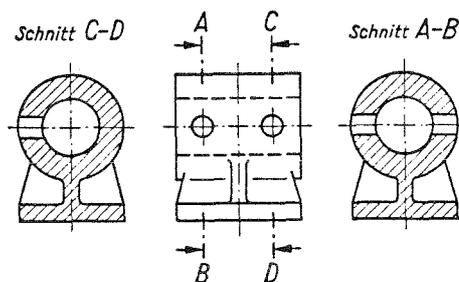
Hinweis auf Projektionen, die auf dem gleichen Plan dargestellt sind
